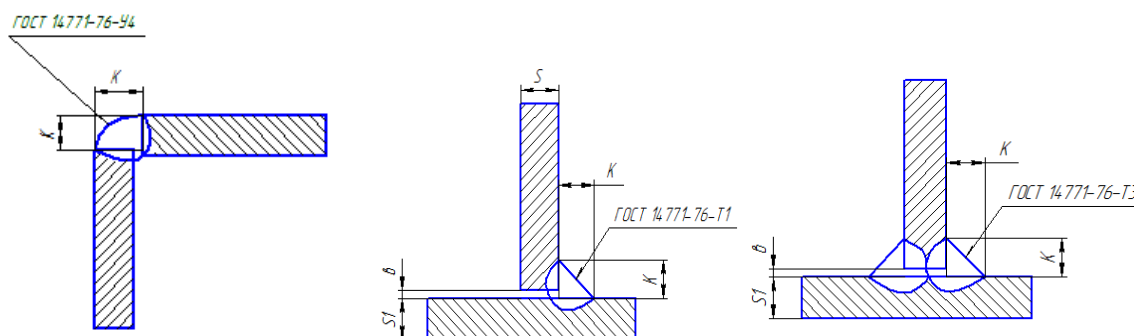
Эскиз подготовки кромок и вид сварного шва
